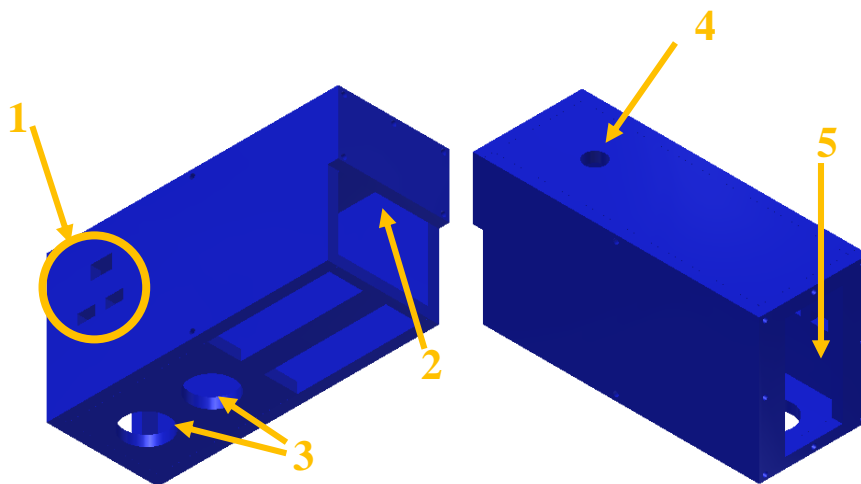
Aberturas de la parte inferior de la carcasa. (Autores)
